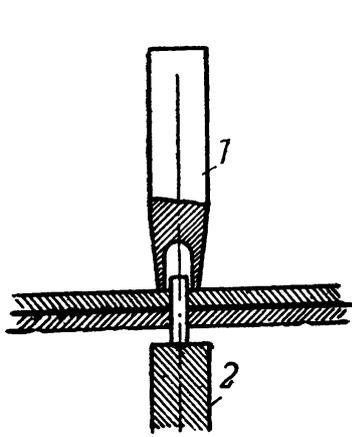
Затягивание заклепки: 1 — затяжка; 2 — подкладка
